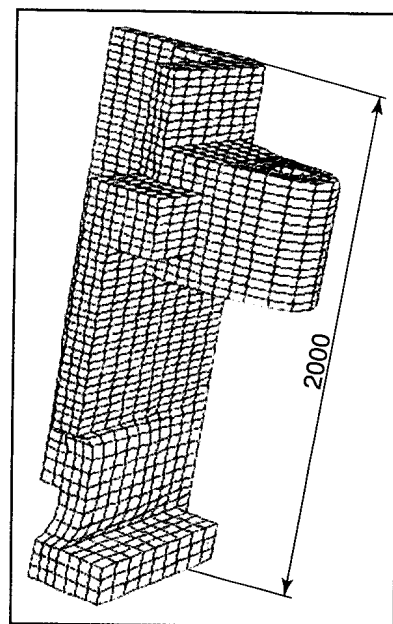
Браковочная дефектность стальной отливки стойки станины кривошипного горячештамповочного пресса
